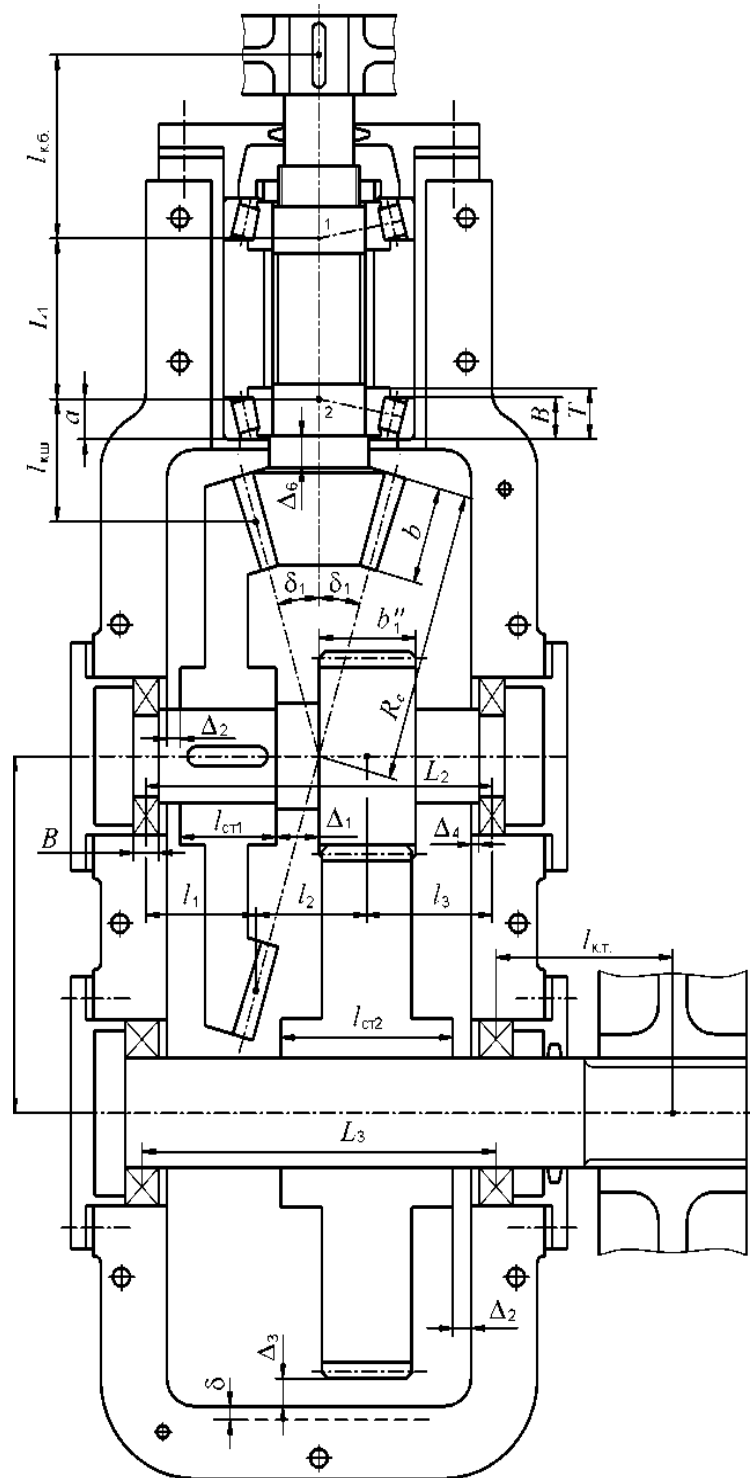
Эскизная компоновка коническо-цилиндрического редуктора
